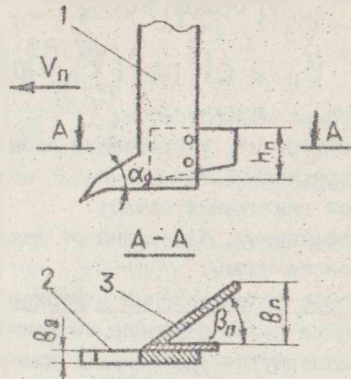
Боковой рабочий орган глубокорыхлителя:
